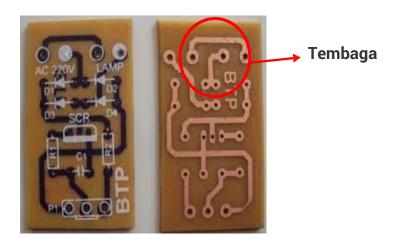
Jenis PCB: Single Layer dan Double Layer
